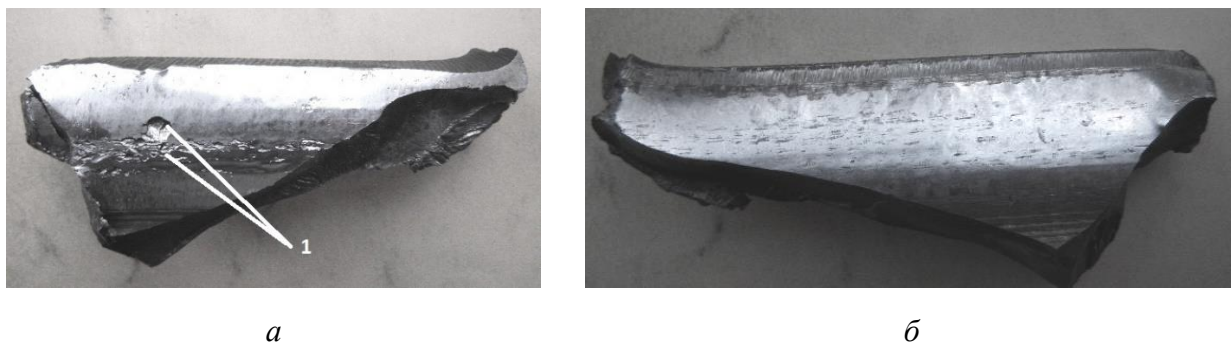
Фрагменты зуба зубчатого колеса: *a* – вид со стороны основной поверхности зуба (1 – питтинги на основной контактных поверхностях зубчатого колеса);
